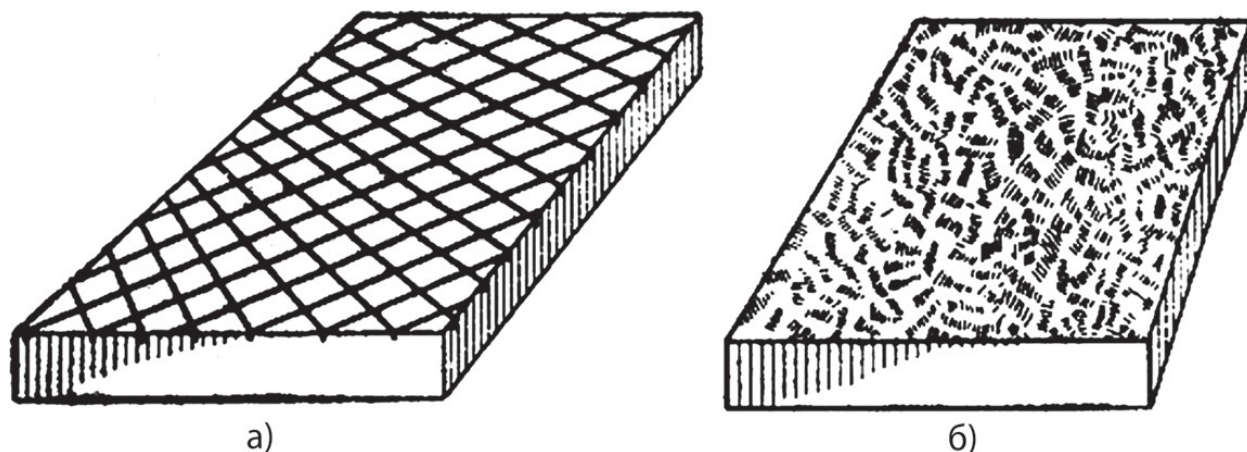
Притиры для обработки плоскостей: а – плита с канавками для грубой притирки; б – плита для чистовой притирки
